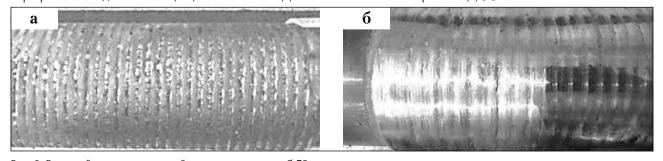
Внешний вид наплавленной поверхности валка Ø 70 мм с неравномерным усилением наплавленных валиков и недостаточным перекрытием соседних валиков (514) после наплавки (а) и после механической обработки (б)
